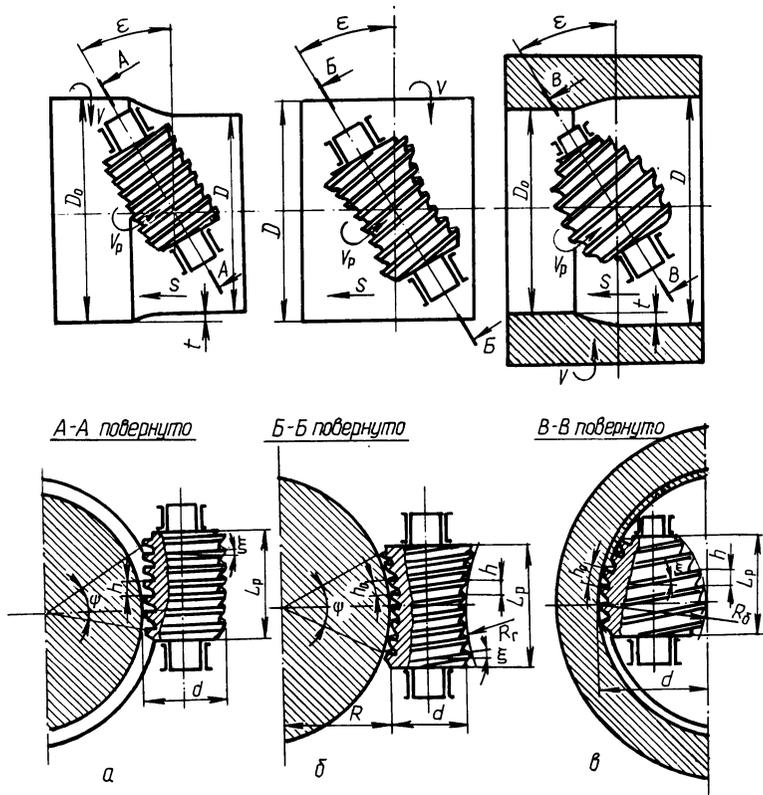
Схемы обработки винтовыми ротационными резцами цилиндрических поверхностей
